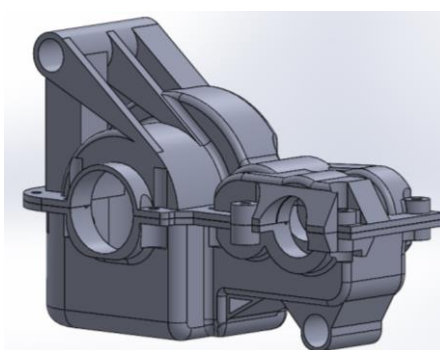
Conjunto da tampa e fundo para caixa adaptada
